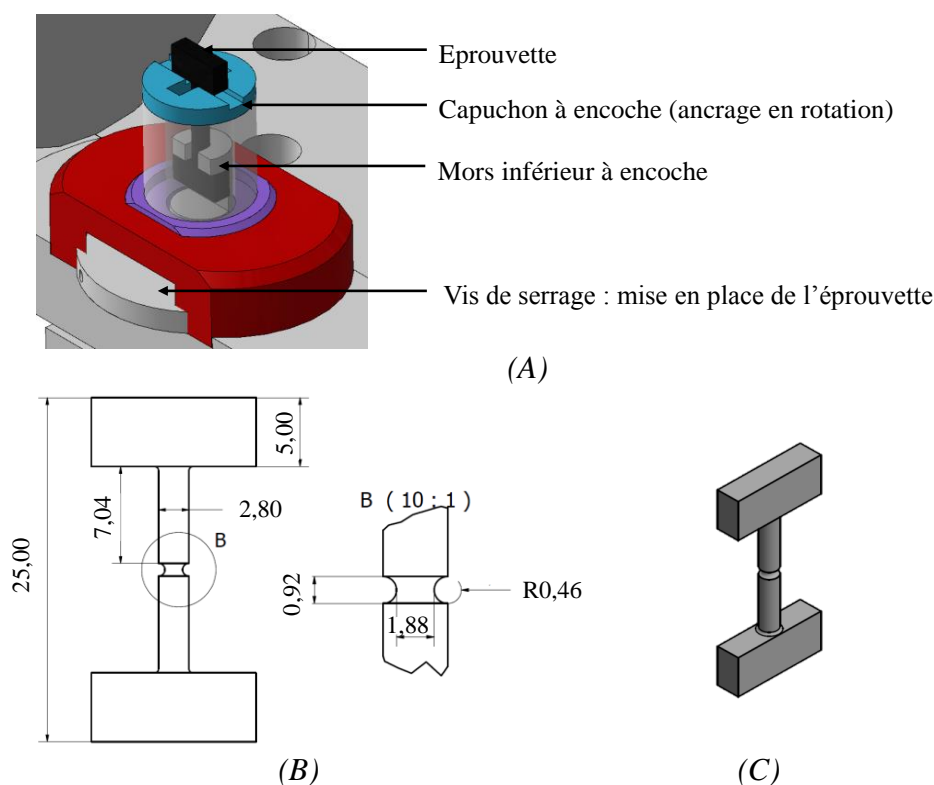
Traction in-situ sur éprouvette axisymétrique entaillée : (A) schéma du système d'encrage, (B) géométrie et dimensions de l'éprouvette et (C) représentation 3D de l'éprouvette
